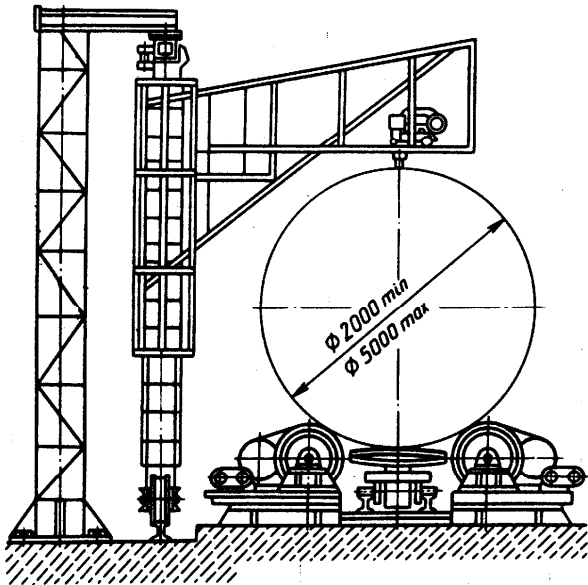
Стенд для автоматической сварки кольцевых стыков
